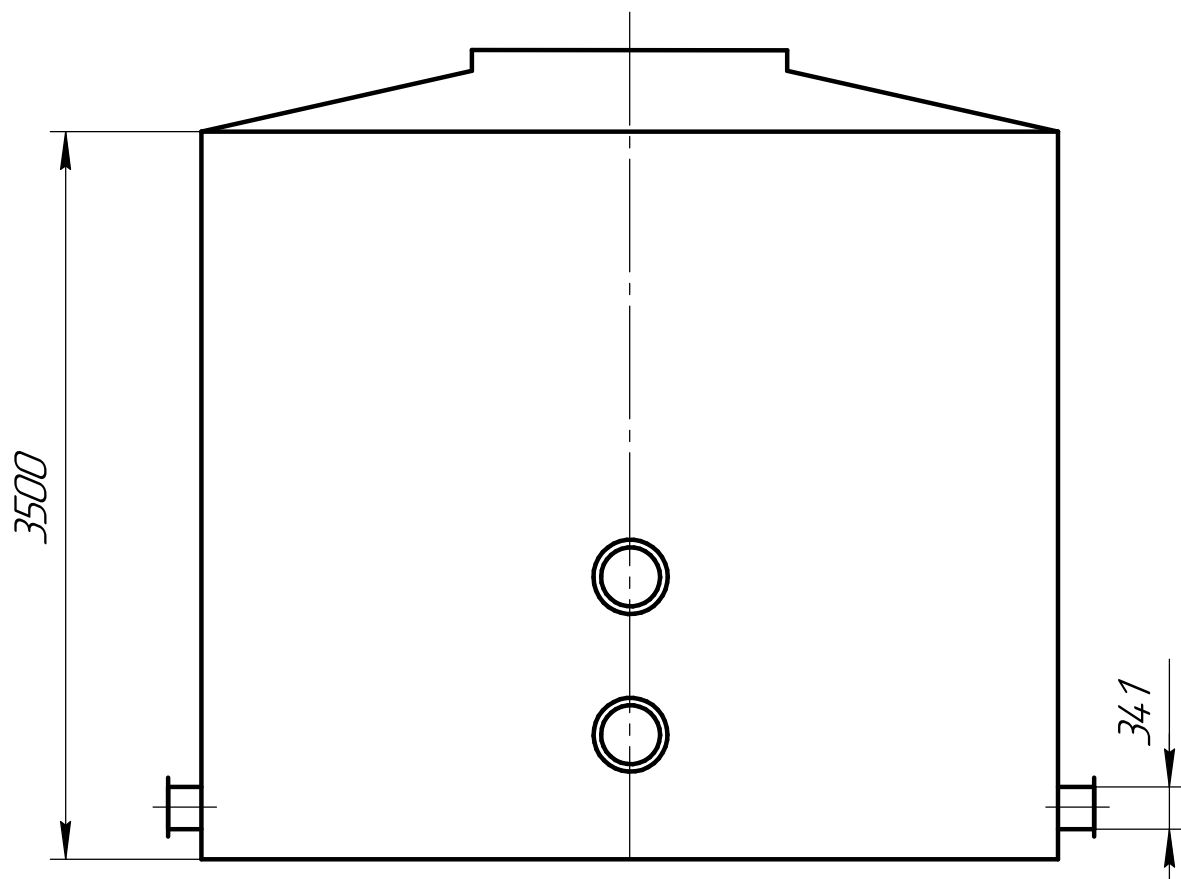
Габаритный эскиз контактного ПГК
